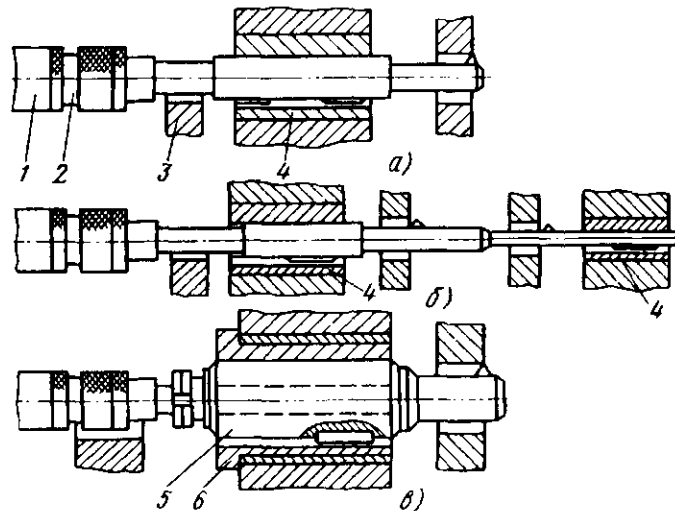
Схемы обработки отверстий с направлением инструмента при плавающем соединении со шпинделем станка: а и б — направление во вращающихся втулках — соответственно одноопорное и двухопорное; в — направление в неподвижной втулке борштанги типа "скользящая втулка"; 1 — шпиндель, 2 — плавающий патрон, 3 — люнет, 4 — вращающиеся втулки, 5 — борштанга типа "скользящая втулка", 6 — неподвижная втулка
